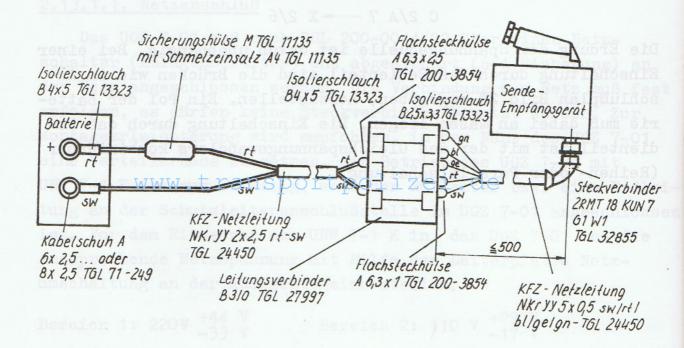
Zweileiterprinzip nicht für die Montage in Fahrzeugen
